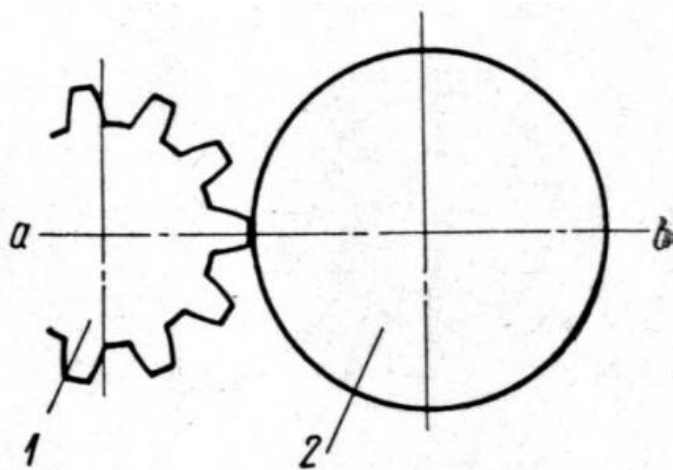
Установка долбяка по наружному диаметру заготовки нарезаемого колеса
